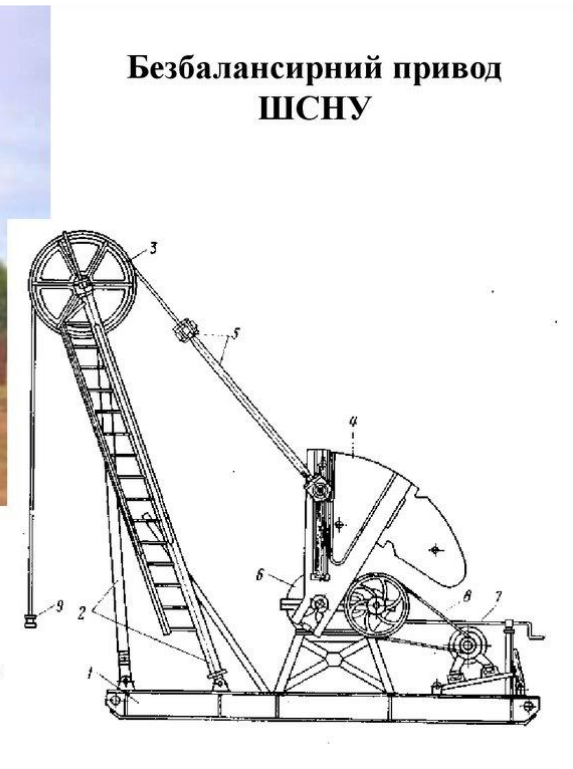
Безбалансирний привід штангової свердловинної насосної установки (ШСНУ)
